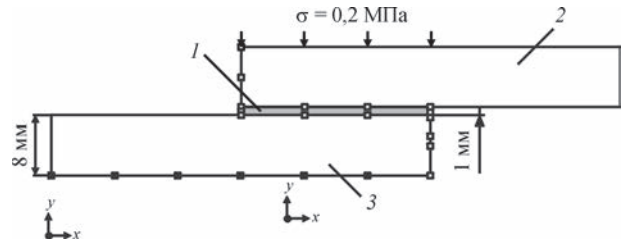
Схема двумерной модели нахлесточного соединения при сварке закладным элементом: 1 — закладной элемент; 2 — образец 1; 3 — образец 2
